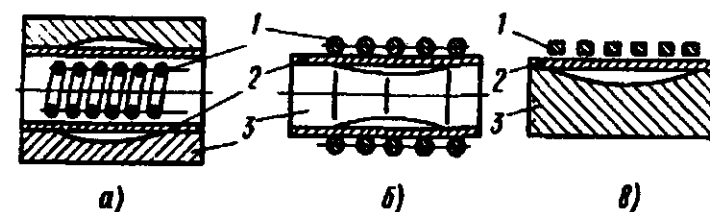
Схемы импульсной магнитной штамповки: а — раздача трубчатой заготовки; б — обжим трубчатой заготовки; в — штамповка-формовка плоской заготовки; 1 — индуктор; 2 — заготовка; 3 — матрица (оправка)
